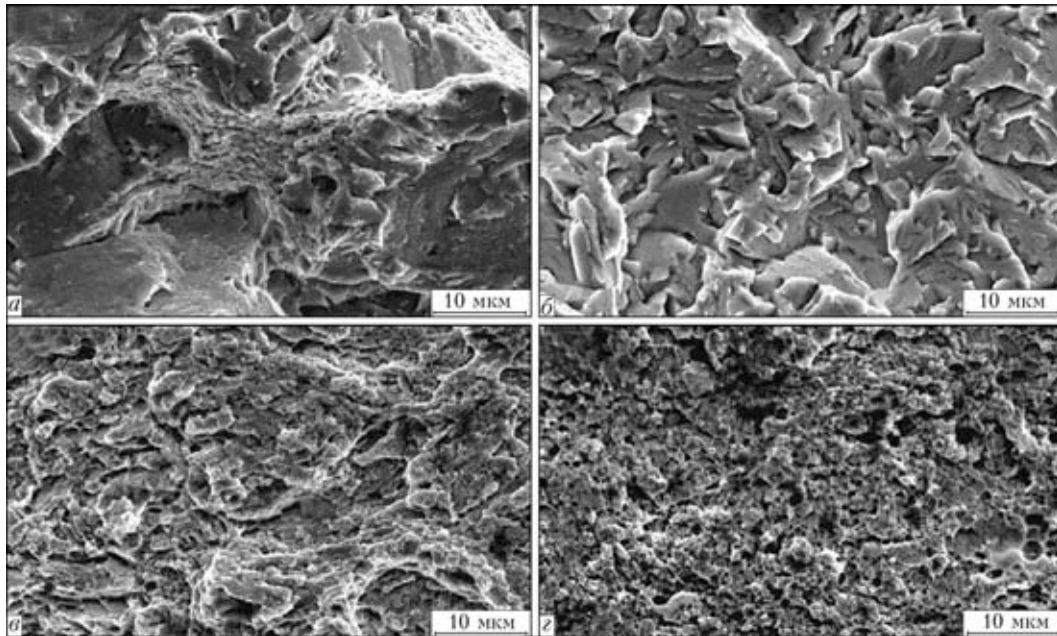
Фрактограммы изломов упрочненных лазерной обработкой образцов после ударного разрушения: а — подложка; б — лазерная закалка (образец № 1); в — лазерный переплав (образец № 2); з — лазерная наплавка (образец № 3)
